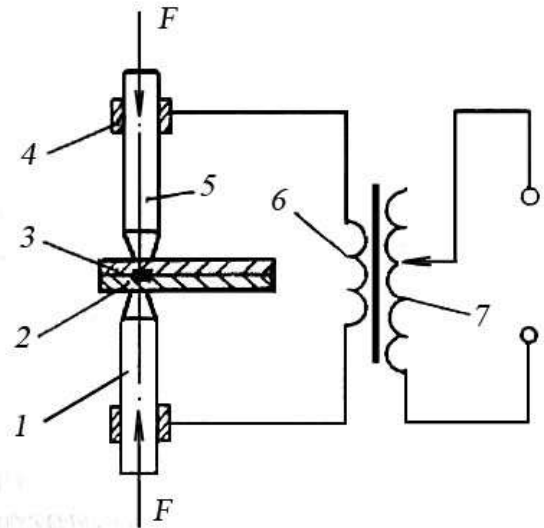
Схема установки для точкового електроконтактного зварювання: 1, 5 - електрод; 2, 3 - зварювана заготовка; 4 - електродотримач; 6 - вторинна і 7 - первинна обмотки трансформатора; F - зовнішня сила
